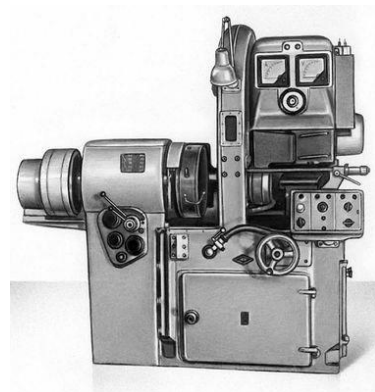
Дісковий анодно-механічний відрізний верстат 4А821
